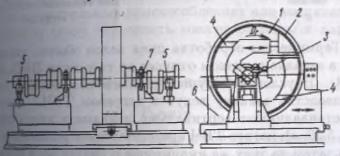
Схема обработки коленчатого вала на токарнодисковом станке
